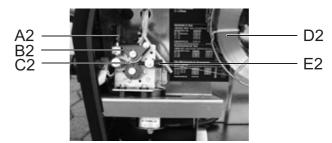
/3. Фрагмент механизма подачи сварочной проволоки.
